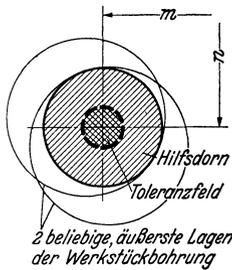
Kreisförmiges Toleranzfeld. Die Mittelpunkte aller Werkstückbohrungen in äußerster Lage liegen auf einem Kreis.
